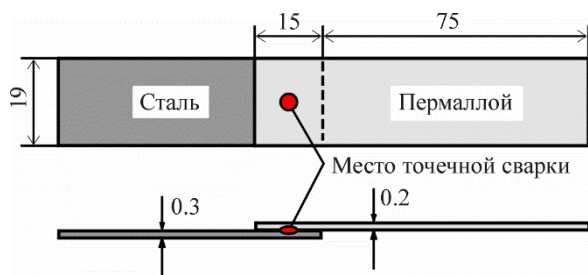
Схема исследованных сварных соединений (размеры приведены в миллиметрах)
